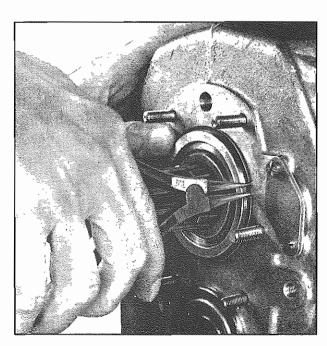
Estrarre l'anello di arresto Withdrawing out the stop ring
